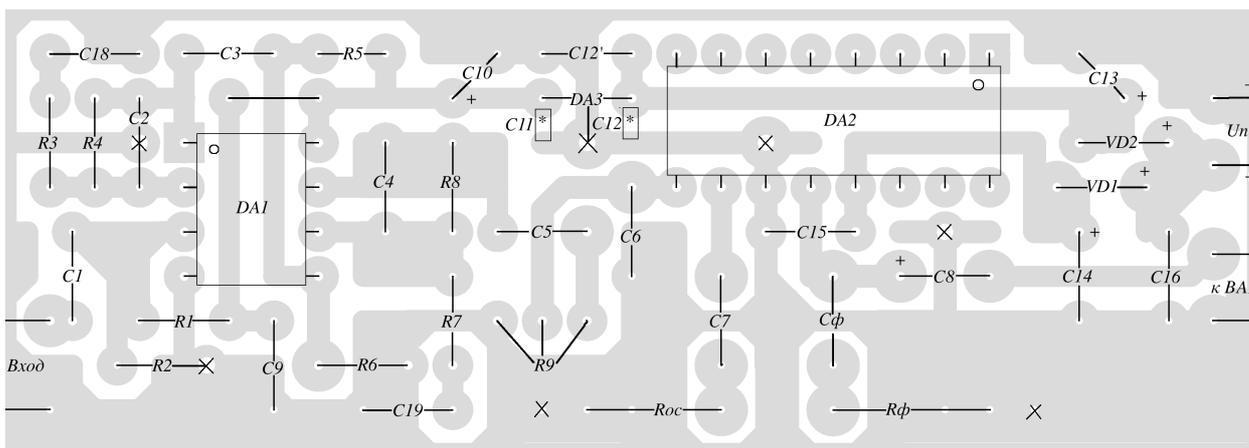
Эскиз расположения деталей на плате усилителя. Знаком \* отмечены элементы, устанавливаемые со стороны печатных проводников. Это – конденсаторы C11 и C12 чип-конструкции типоразмера 0805 (плюс-минус один типоразмер), которые впаяются между печатными проводниками общего провода и “плюсом”, непосредственно у выводов ИМС DA3. На плате предусмотрены отверстия под дополнительный конденсатор C12’ 1 мкФ для случая сильных РЧ наводок и под цепочку из последовательно соединённых конденсатора Cφ и резистора Rφ, соединяющих выход ИМС (вывод 12) DA2 с общим проводом. Крестиками обозначены места соединения фольги с нижней и верхней стороны платы.
